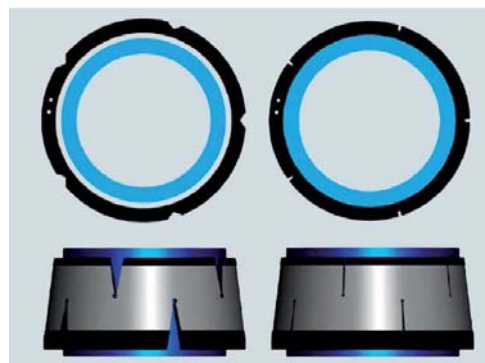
Принцип работы конической сварочной манжеты: разрезы обеспечивают возможность эластичного уменьшения диаметра при заполнении кольцом зазора между трубой и муфтой.
